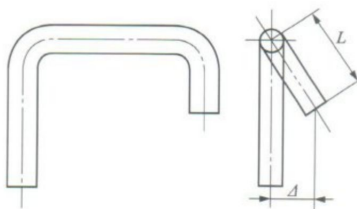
Π 形弯管的平面度偏差示意图
